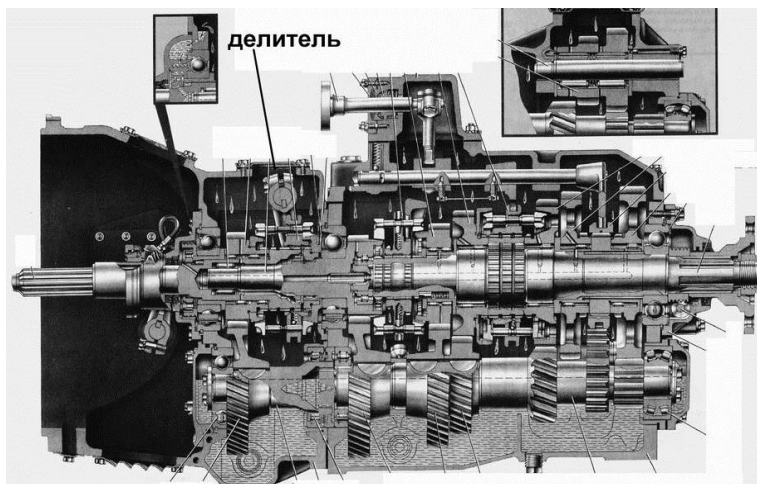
Пятиступенчатая коробка передач с делителем
